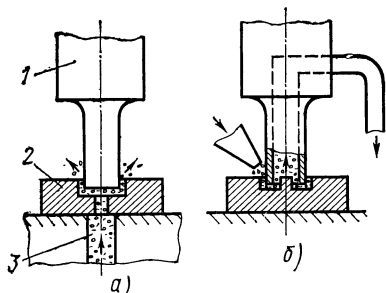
Схема ультразвукового резания с нагнетанием (а) и отсосом (б) абразивной суспензии: 1 — концентратор-инструмент, 2 — заготовка, 3 — абразивная суспензия
